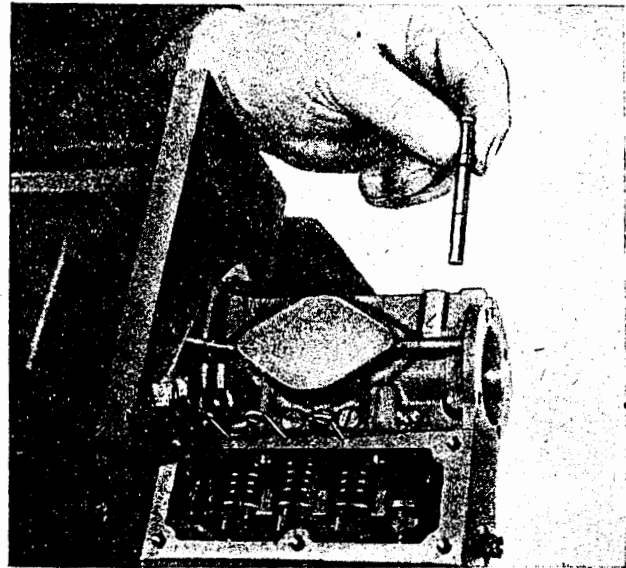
Richtiges Einsetzen der Pumpenkolben
